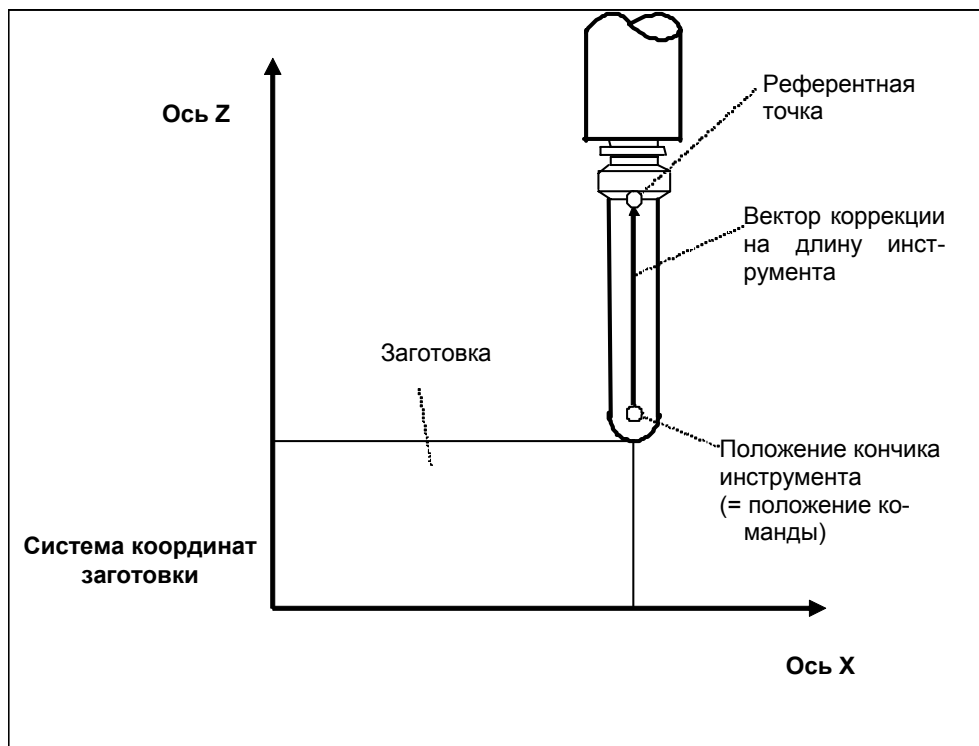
(e) Резка вершиной инструмента, когда отсутствует погрешность установки заготовки
